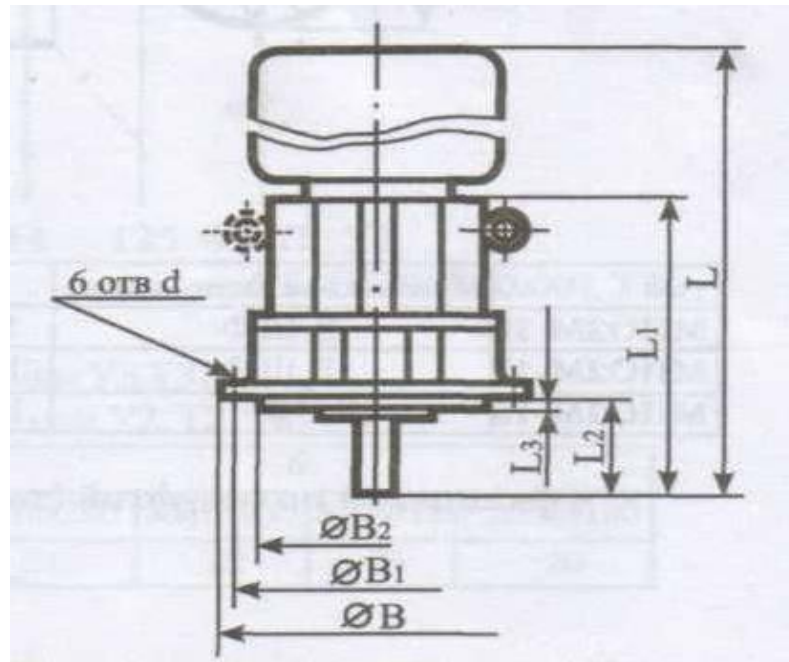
Загальний вид планетарного мотор-редуктора
